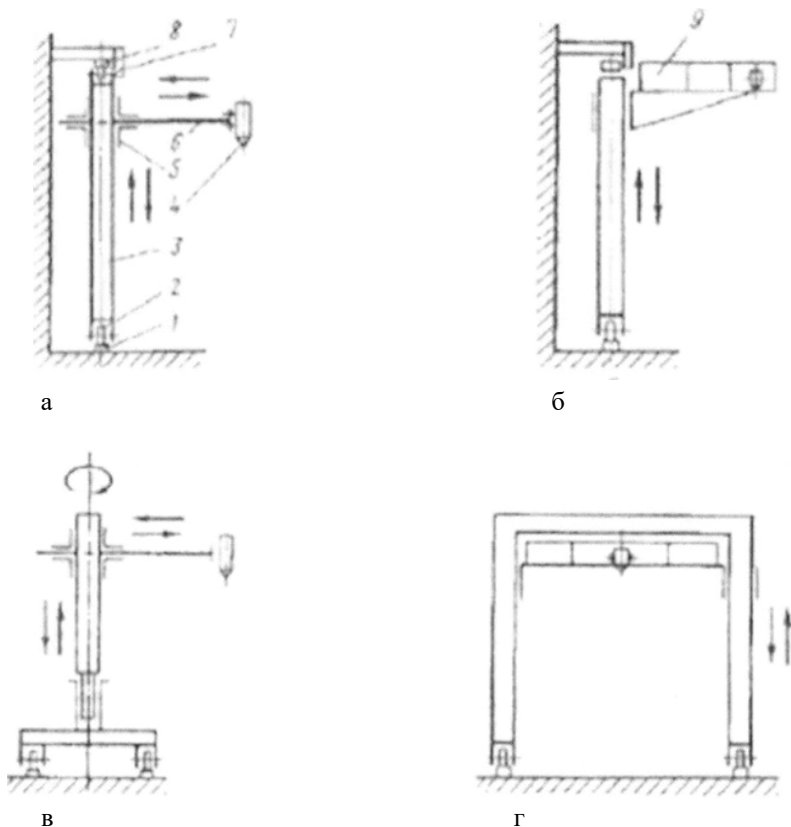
Схемы тележек для сварочных аппаратов: *а, б* – велосипедные; *в* – глгольная; *г* – порталная; *1, 8* – рельсы; *2, 7* – катки; *3* – колонна; *4* – сварочная головка; *5* – каретка; *б* – консоль; *9* – балка
